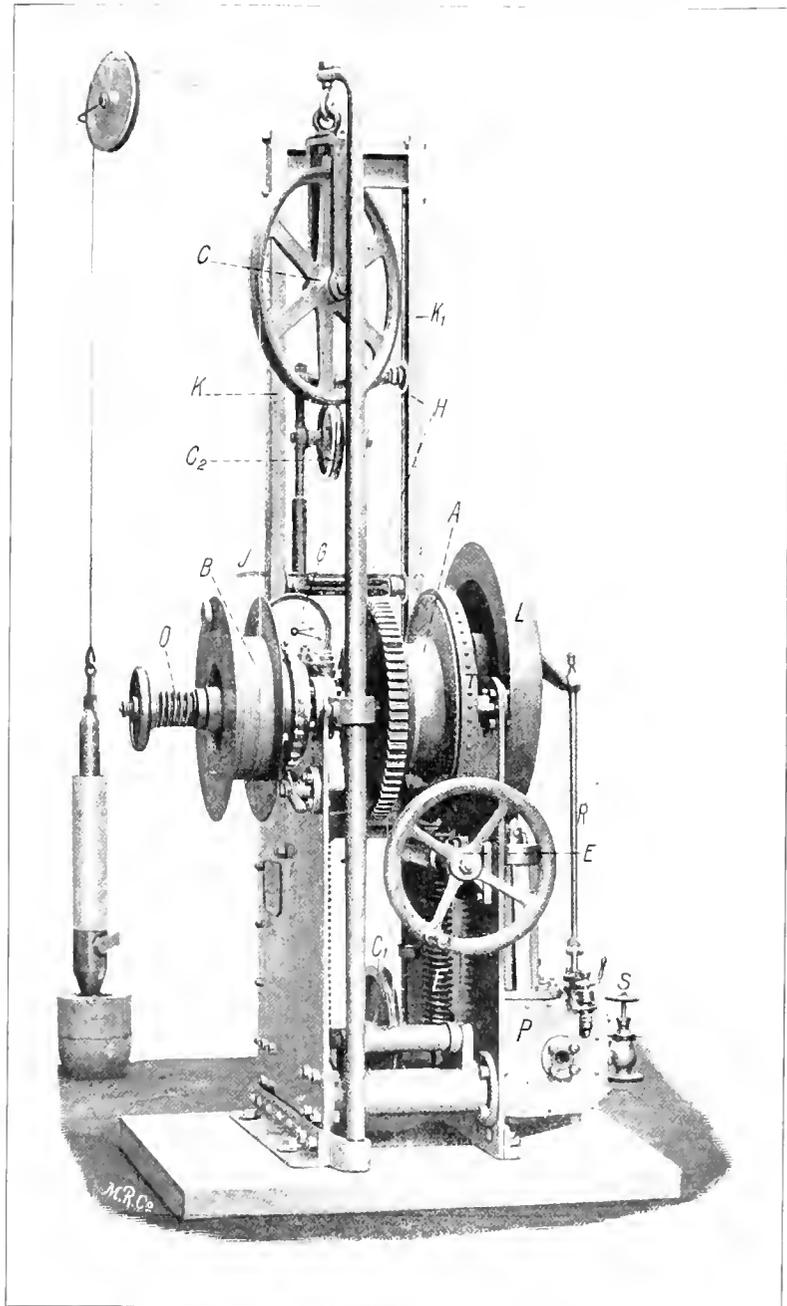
Gesamtansicht der LE BLANC'schen Maschine.
